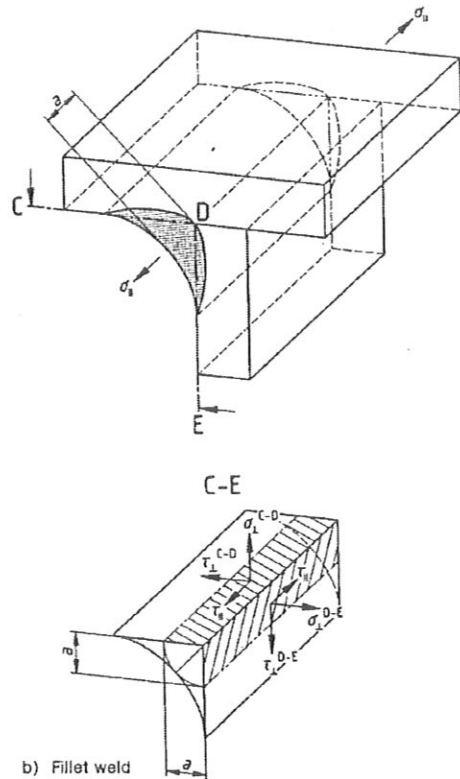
assemblage soudée (selon DIN 18 800-1)
